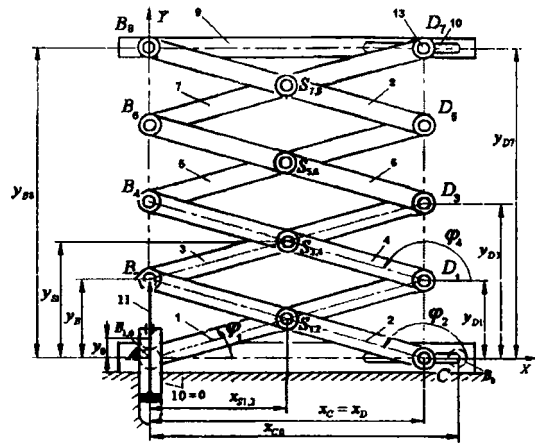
Кинематическая схема рычажного механизма ножничного подъемника
